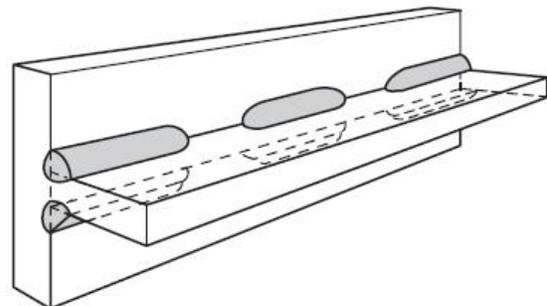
Nomenclatura Secuencia de Soldadura
